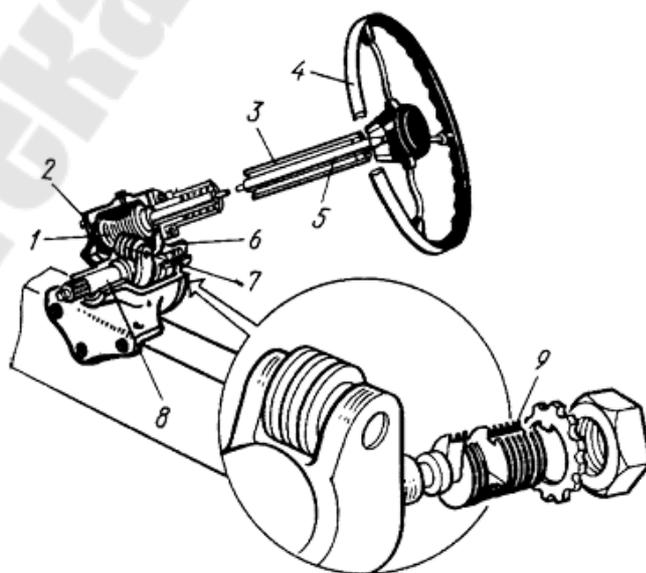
Рулевой механизм автомобиля ГАЗ–53А
